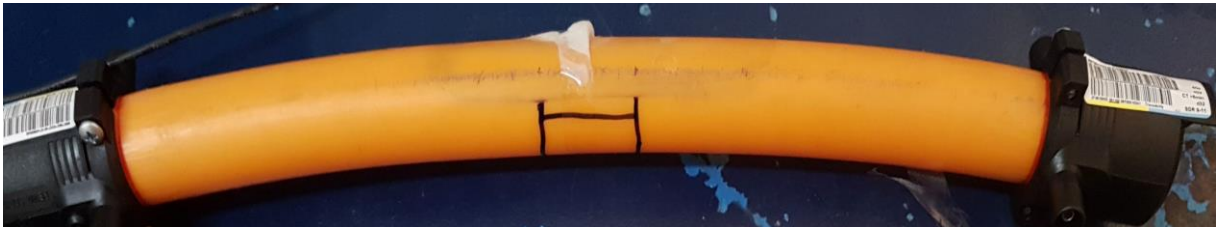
POSICIONAMENTO DO CP NA BANCADA DE USINAGEM
